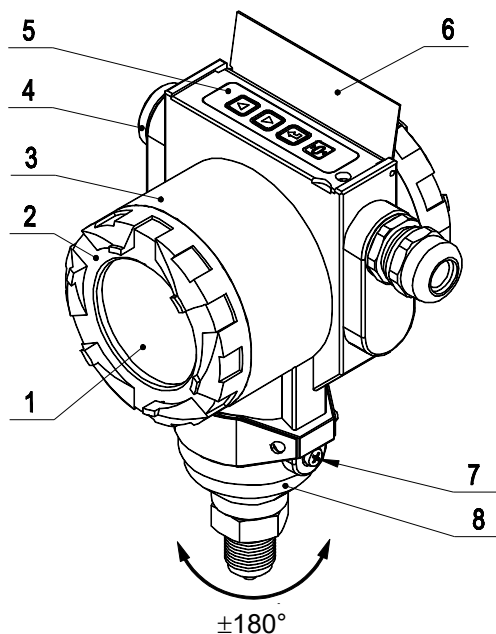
Общий вид АИР-30М (корпус АГ-19)
